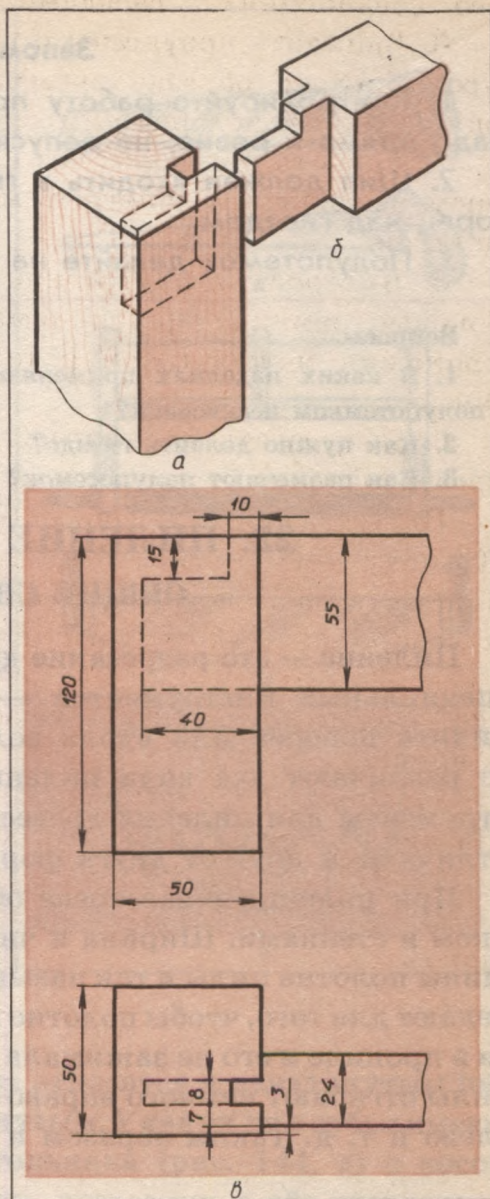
Угловое концевое соединение на шип с полупотемком несквозной: а — деталь с выдолбленным гнездом; б — деталь с шипом; в — соединение деталей.
